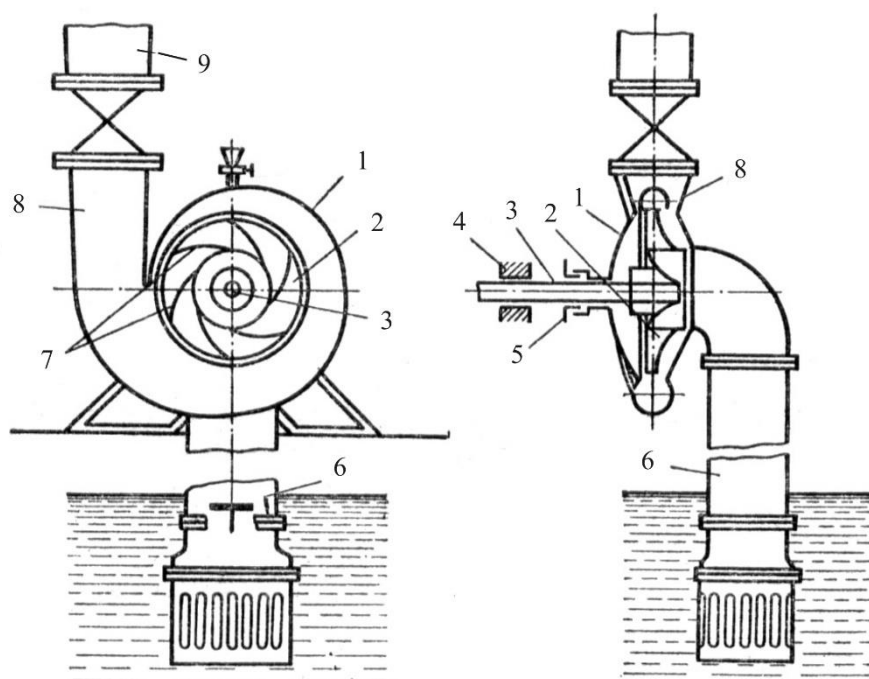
Центробежный насос: 1– спиральный корпус; 2 – рабочее колесо; 3 – вал; 4 – подшипники; 5 – сальники; 6 – всасывающий патрубок; 7 – лопатки рабочего колеса; 8 – нагнетательный патрубок; 9 – напорный трубопровод
